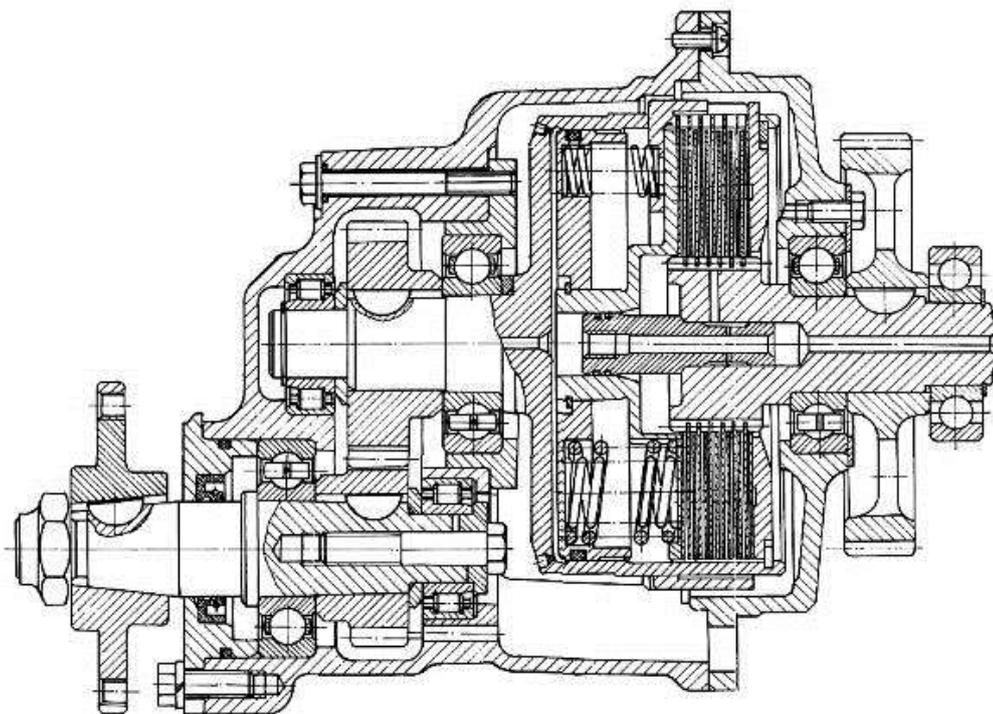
Привод вентилятора двигателей 8437.10, 8491.10-032, 8492.10-033
